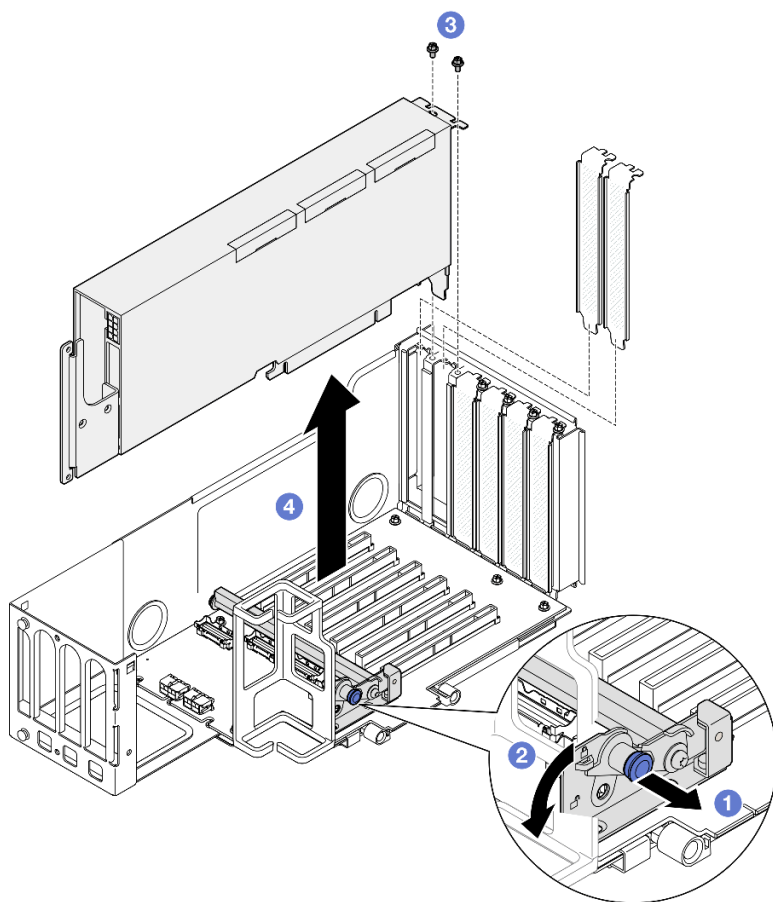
Removendo o adaptador de GPU da placa riser PCIe
